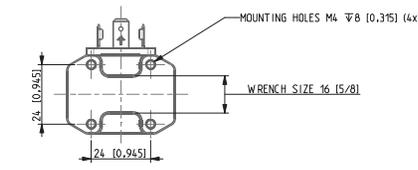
Dimensioni 1/4" in linea, larghezza bobina 32
